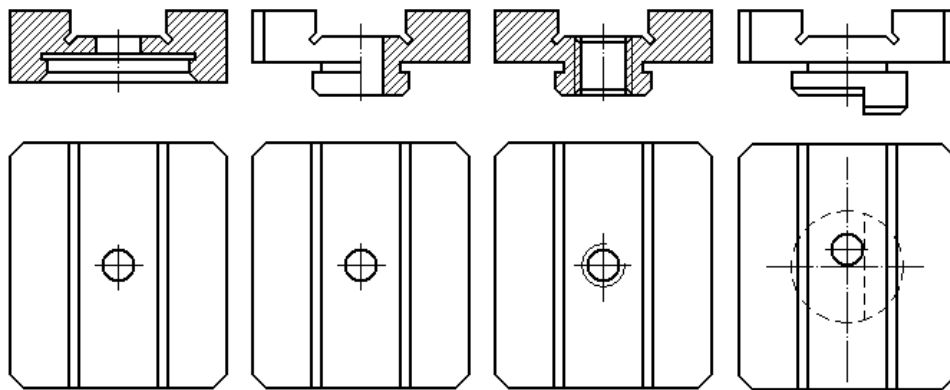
Направляющий паз с отверстием как конструктивный инвариант условной совокупности деталей
